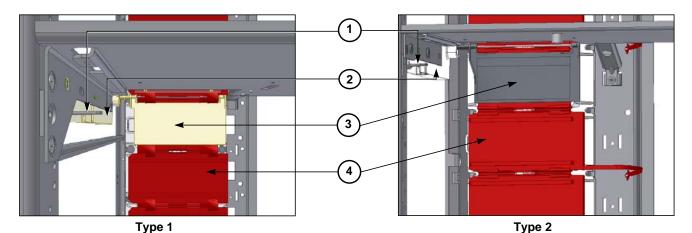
Emplacement du couvercle de volet automatique pour une ouverture de panneau latéral
